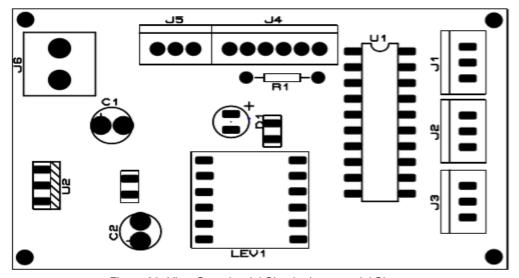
Vista Superior del Circuito Impreso del Sistema. Fuente: Autor.
